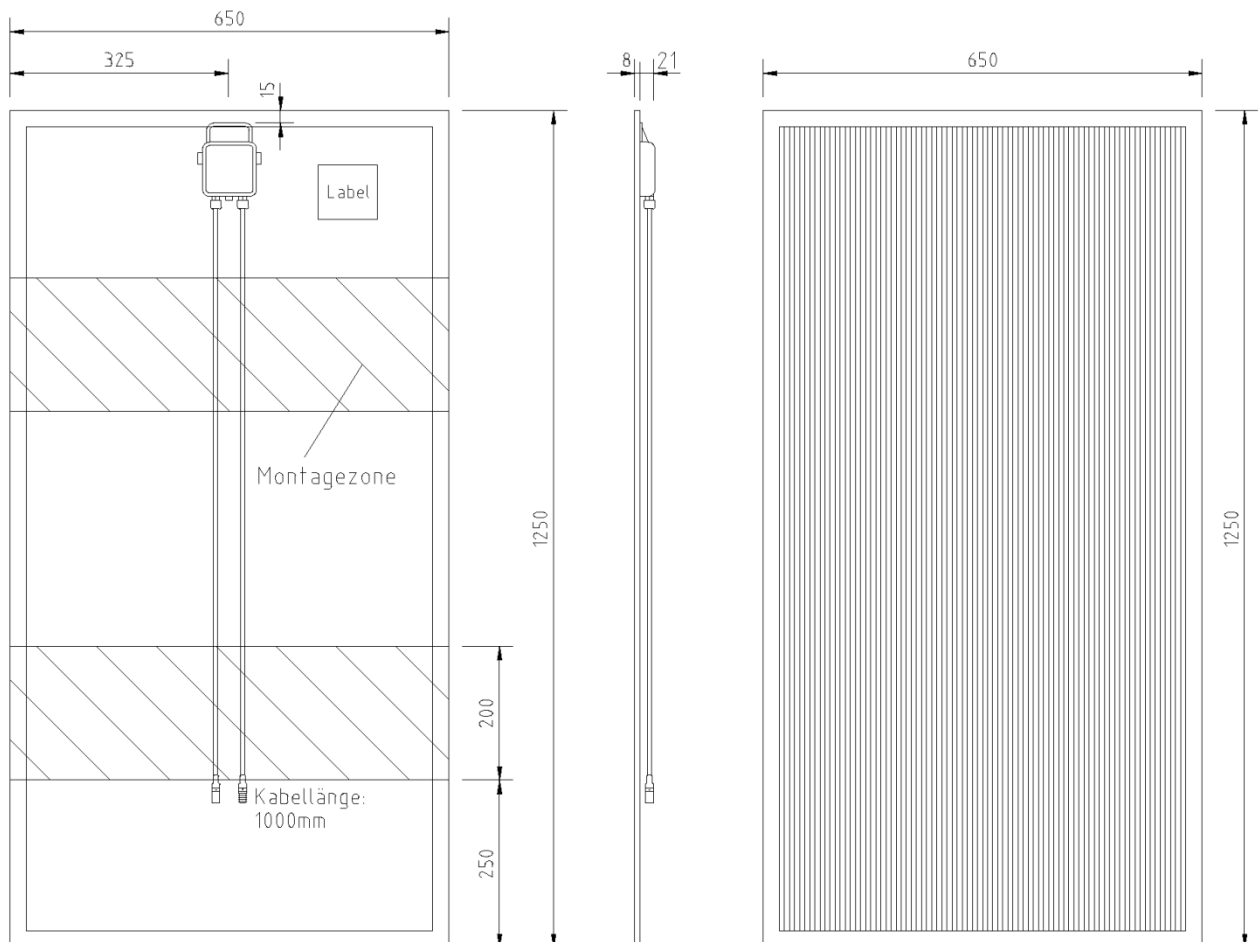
Technische Zeichnung für PV Module der Serie SCG-HV-L und SCG-LV-L
